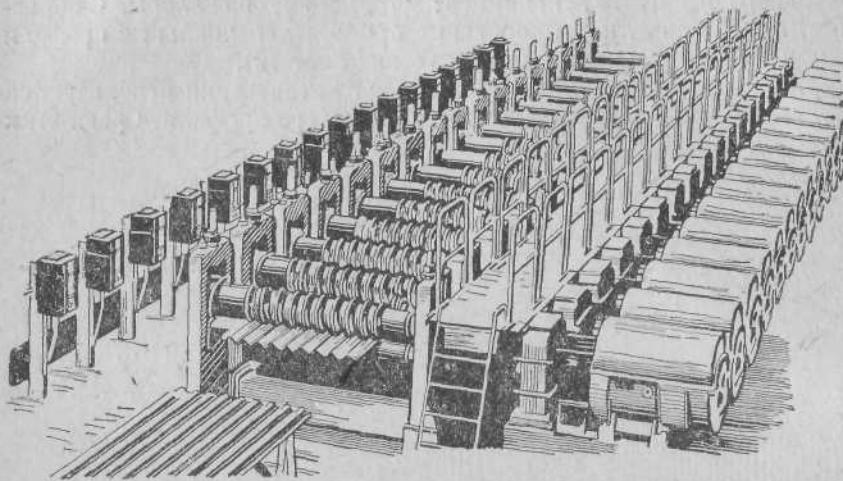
Профилегибочный стан для профилирования ребристых плит, волнистых листов, различного типа обшивок.
